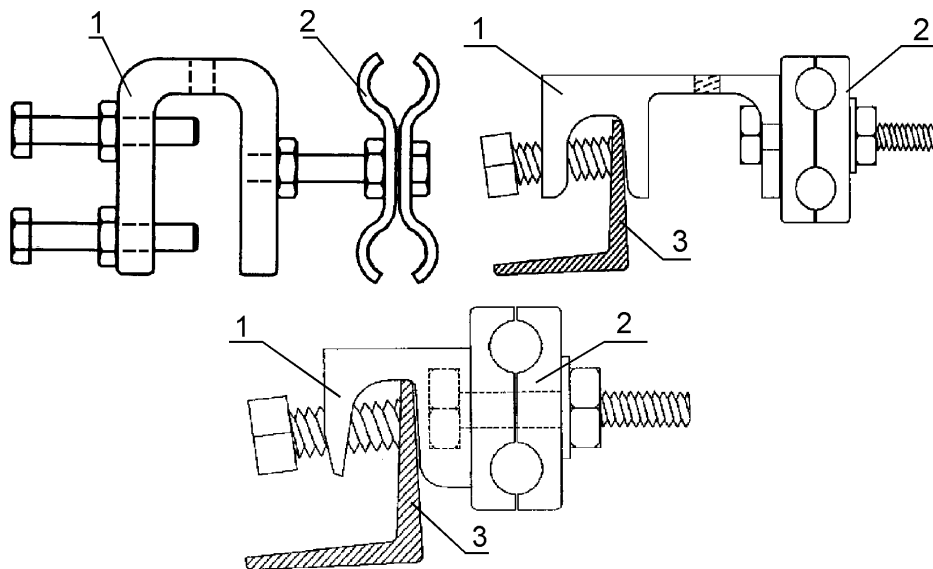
Різновиди струбцин для закріплення підтримувальних затискачів шлейфового типу: 1 - струбцина; 2 - підтримувальний затискач шлейфового типу; 3 - елемент конструкції металевої опори
